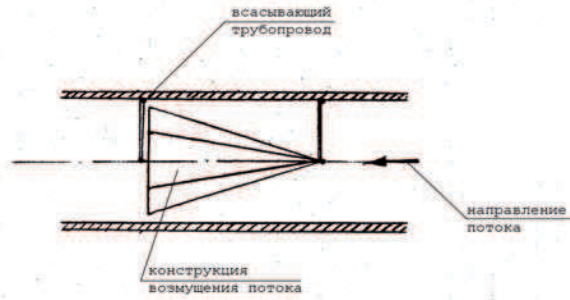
Схема установки конструкции возмущения потока в трубопровод обратной промывки
